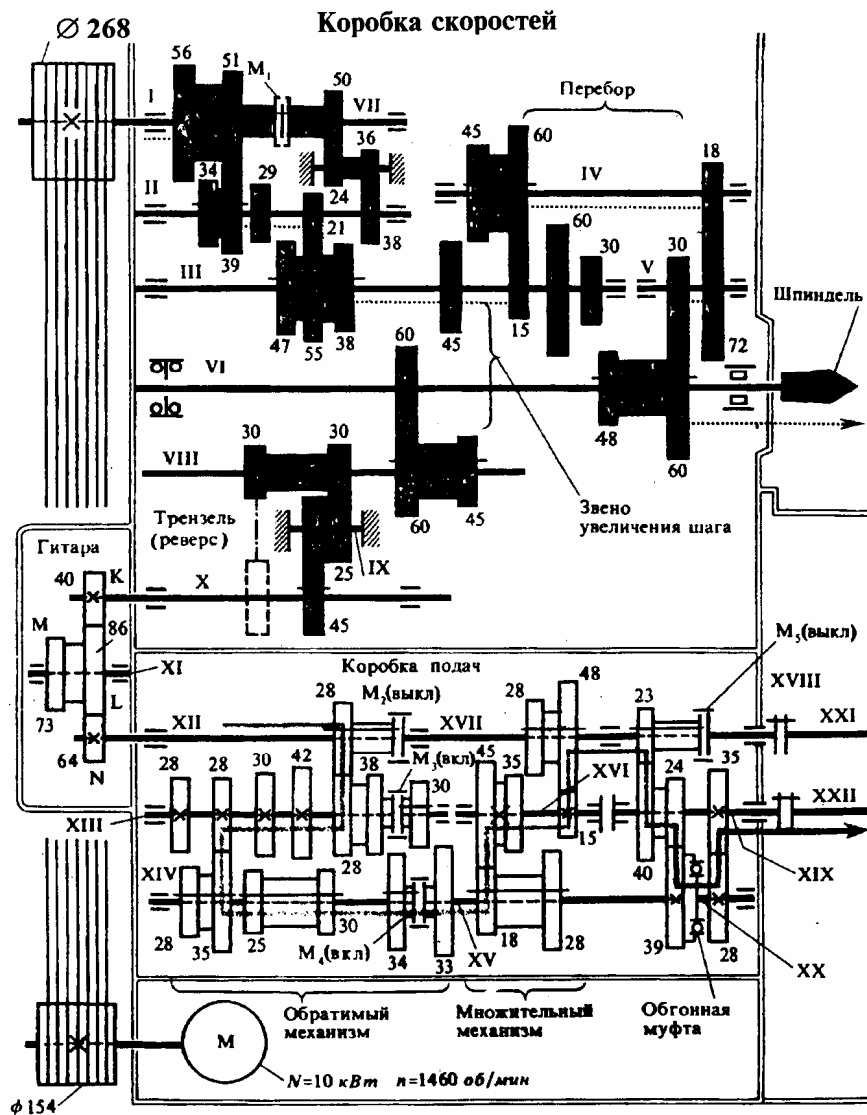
Кинематическая схема токарно-винторезного станка 16K20
